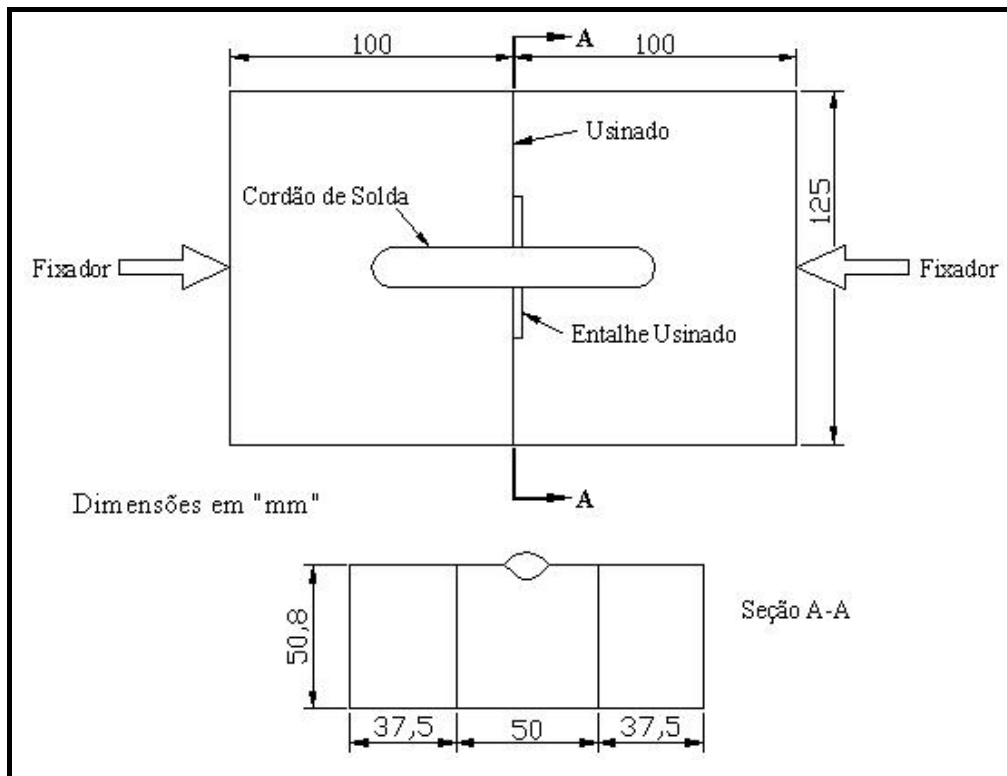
Desenho do corpo de prova ⁽⁹⁾.
